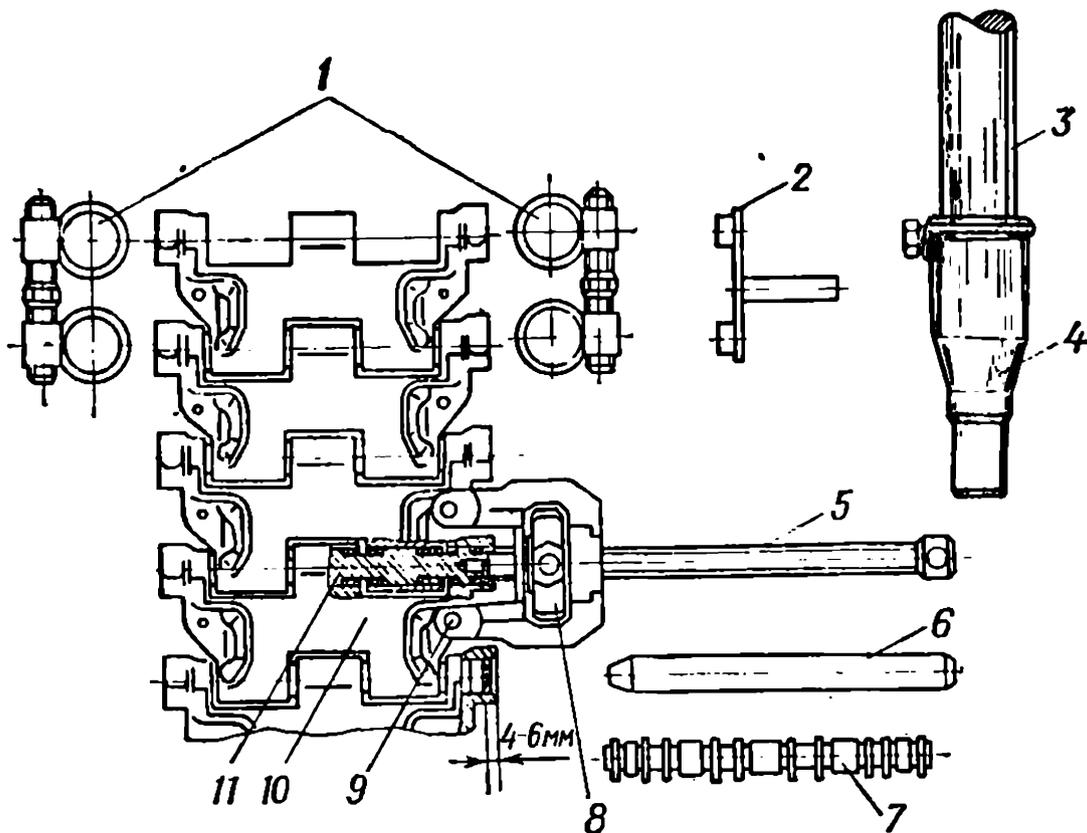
Установка комплекта приспособлений для замены пальцев гусеницы с закрытым шарниром:
